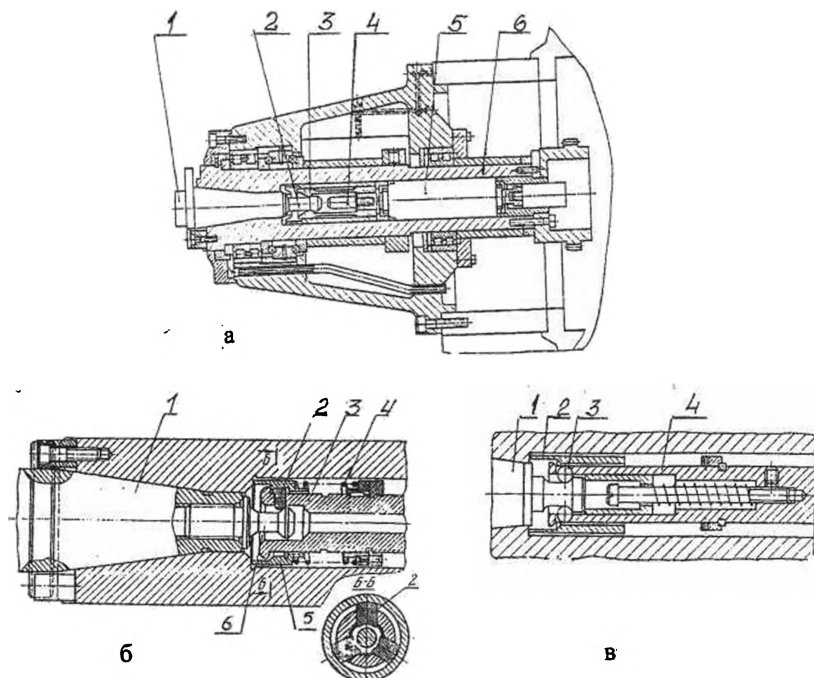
Види механізмів для захватування інструментальних оправок:
